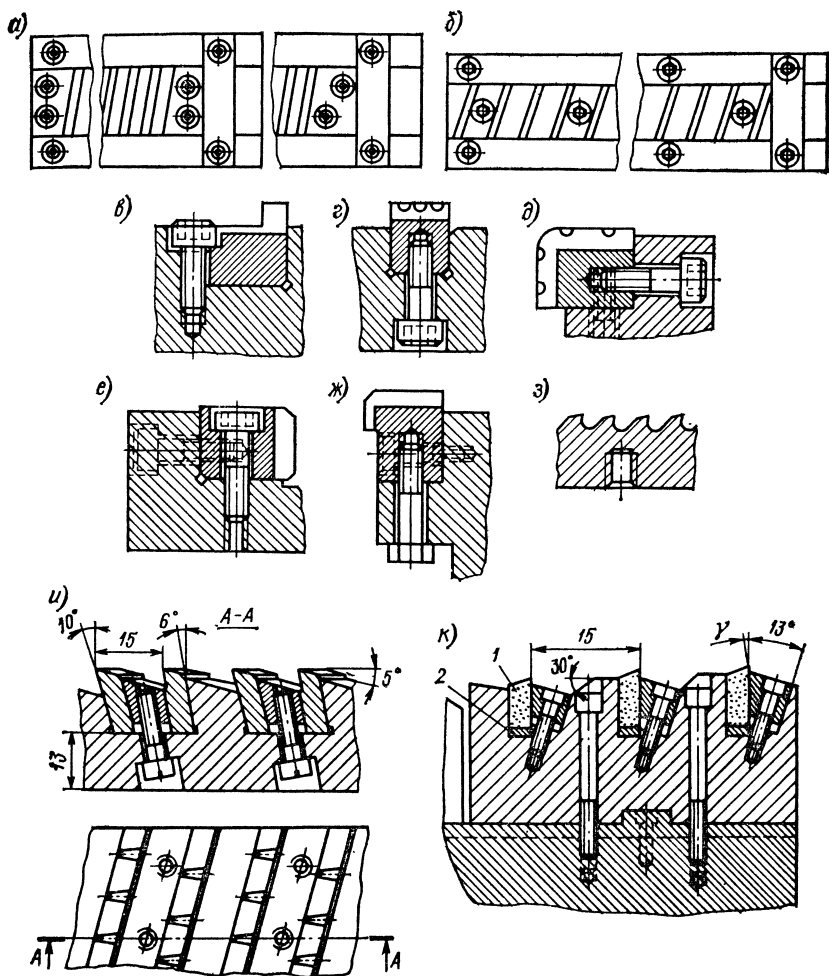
Варианты крепления режущих элементов сборных плоских протяжек: *a* — винтами сверху по концам секции; *b* — то же, вдоль секций; *c* — краем головок винтов; *e* — винтом снизу; *d*—*ж* — одновременно с двух сторон; *в* — резьбовое отверстие с плоским дном; *и* — одновременное крепление двух твердосплавных пластин; *к* — крепление по одной твердосплавной пластине
